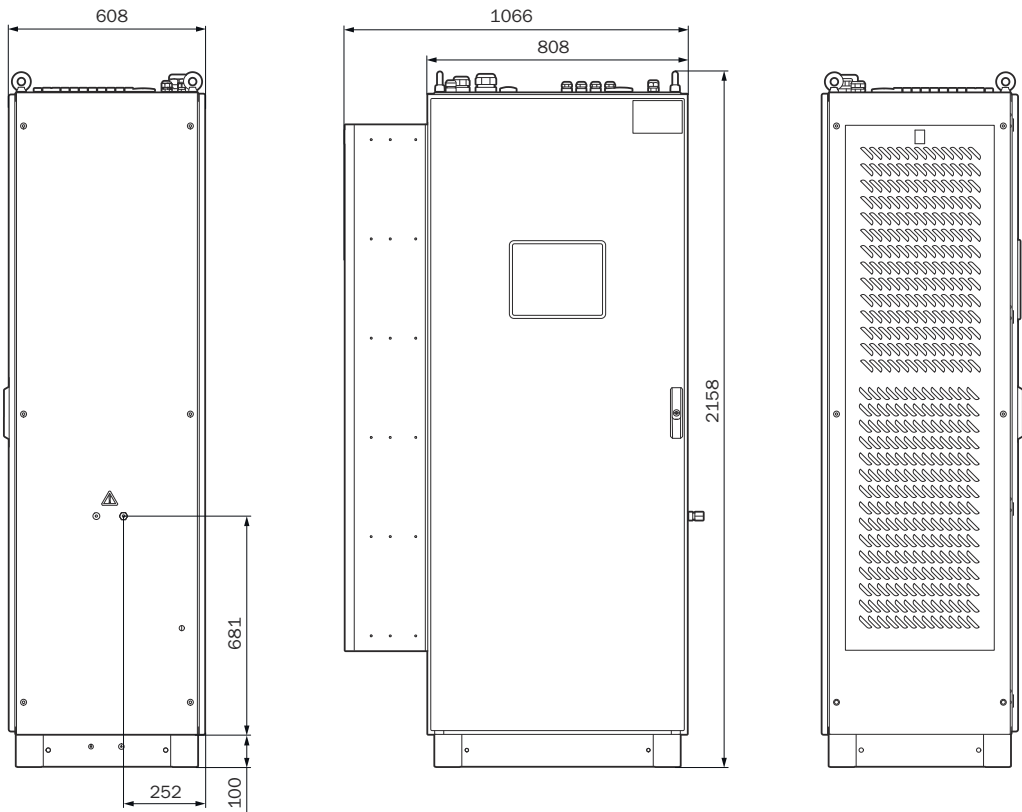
MCS200HW i grundkonfiguration (mål i mm)
